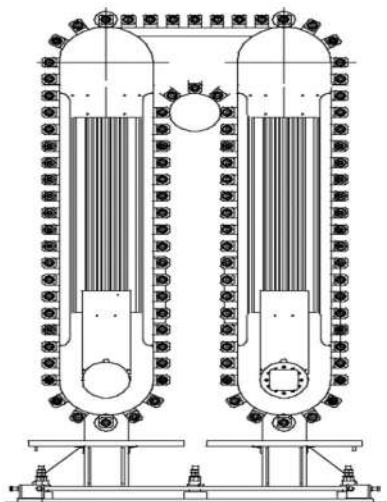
Ланцюговий інструментальний магазин верстата HURON KX 100
